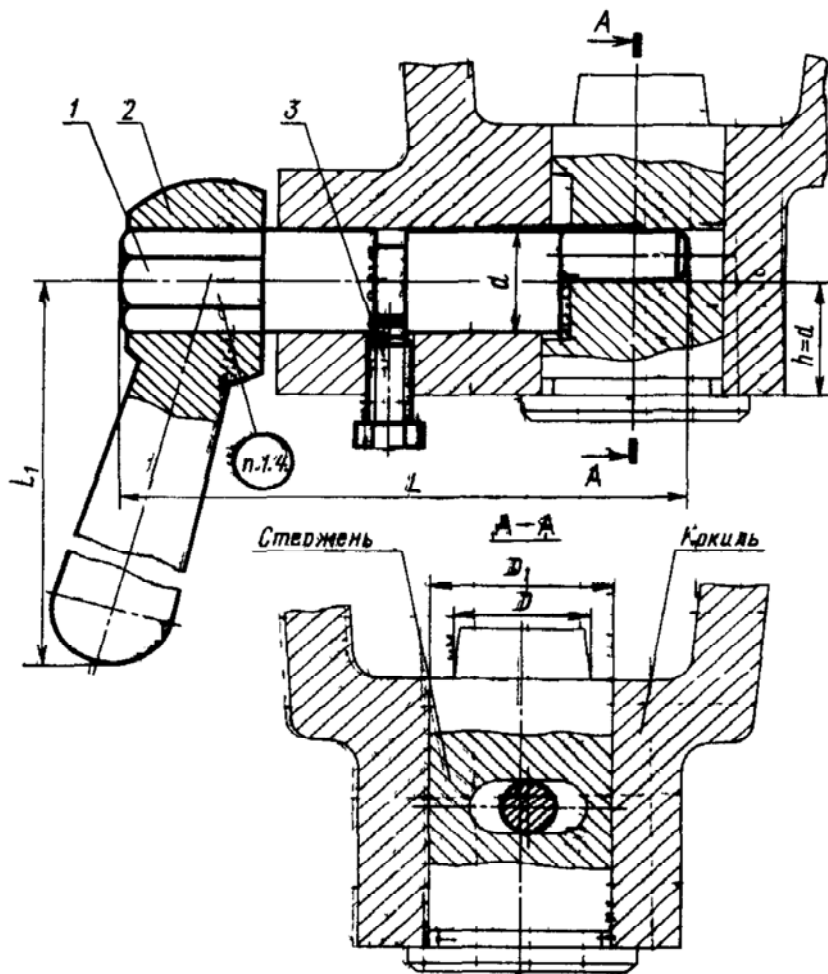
Конструкция приспособления для удаления стержней консольным эксцентриком
